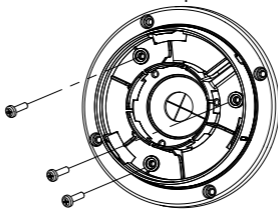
Крепление винтов на крышке монтажной коробки
